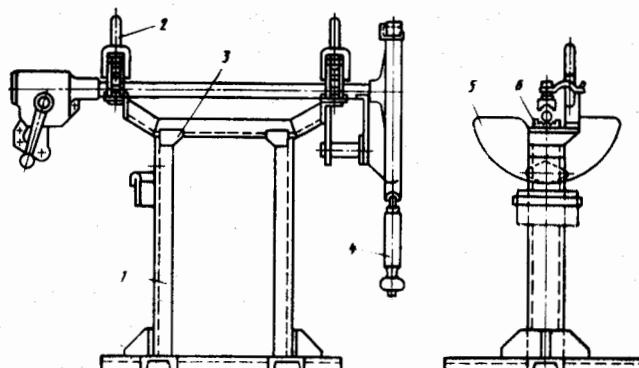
Стенд для сборки и регулировки рулевых механизмов
